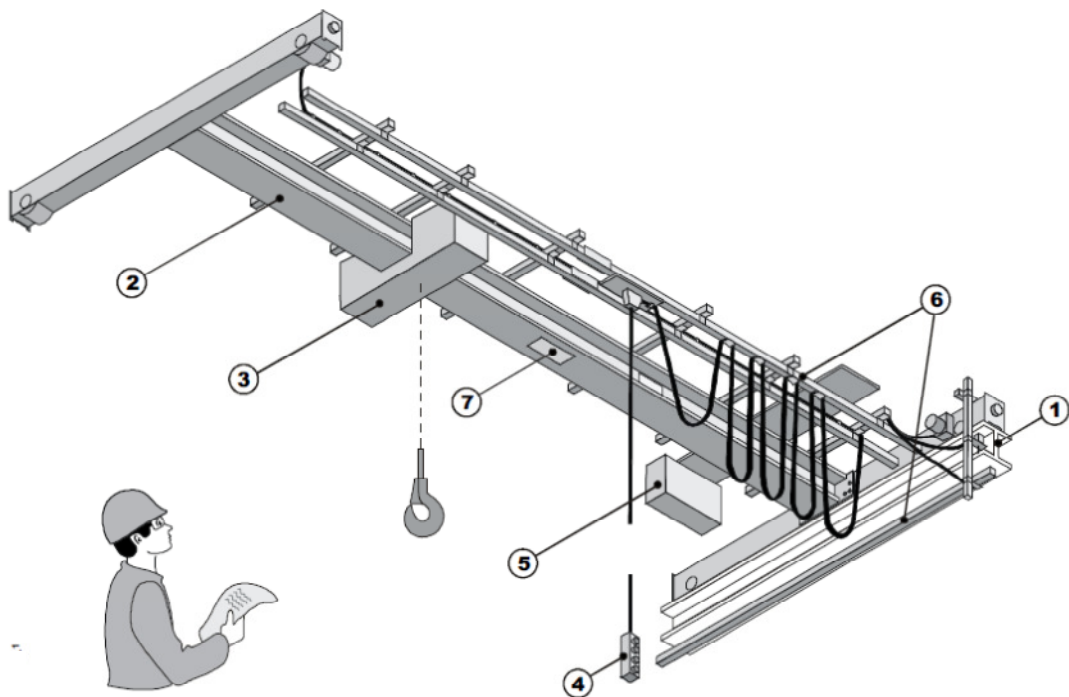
Pont Roulant mono poutre (15 tonnes)
